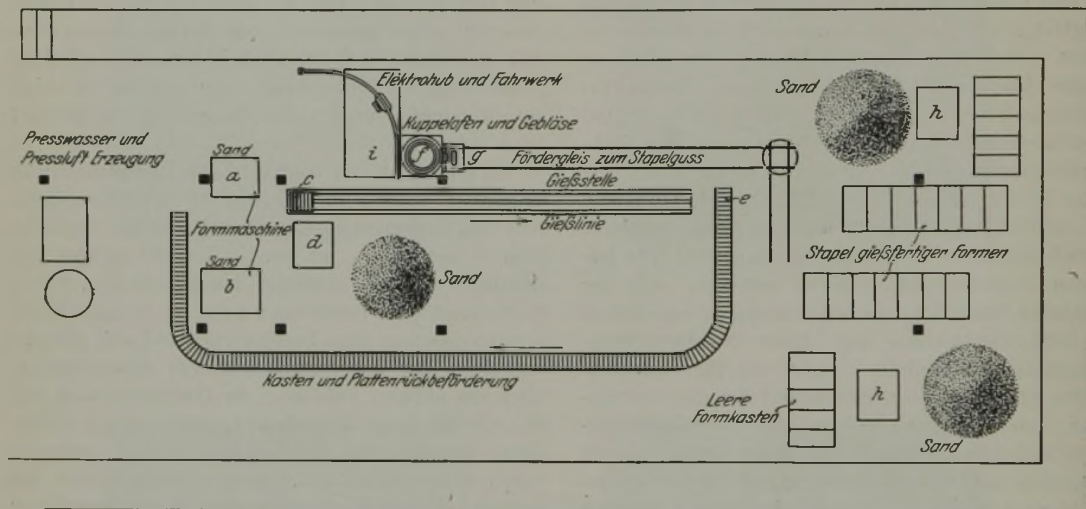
Lageplan der „Gießerei in Betrieb“.
